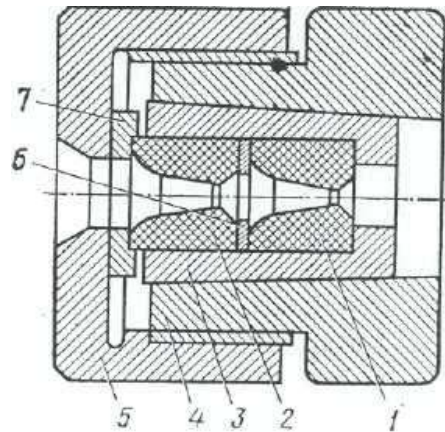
Збірна волока для волочіння дроту в режимі гідродинамічного тертя: 1 – робочий твердосплавний вкладиш; 2 – напірний вкладиш; 3 – затискнавулка; 4 – корпус; 5 – гайка; 6 – ущільнення; 7 – завзята шайба
